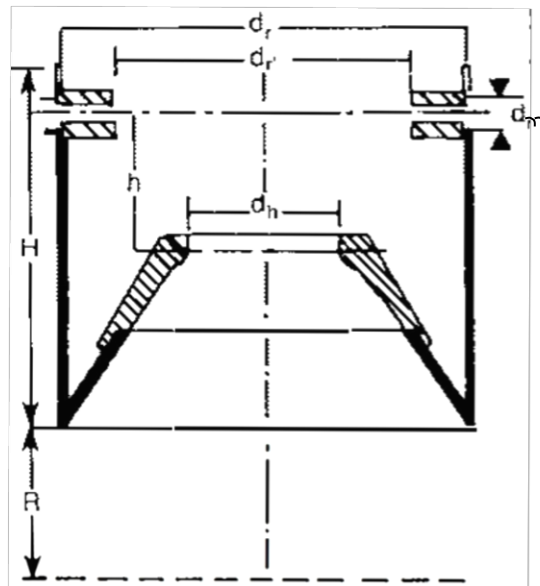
Hauptabmessungen im Reaktor laut Kaupp [28]
